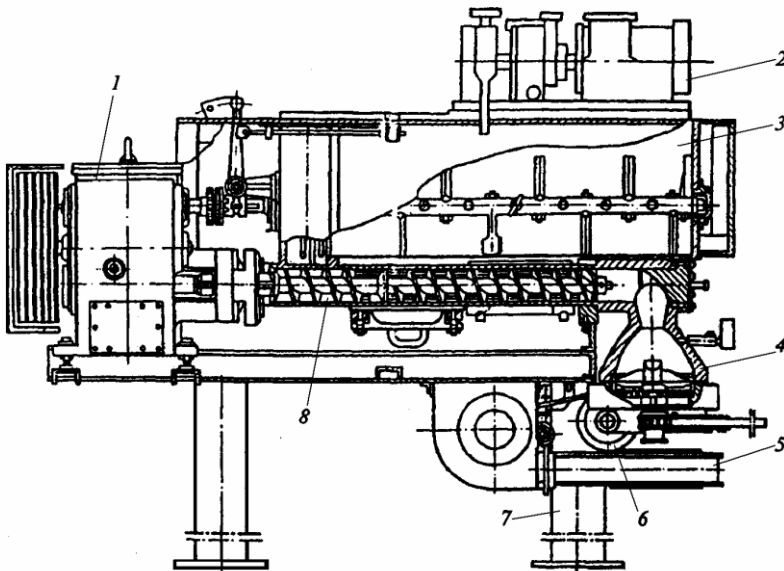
Шнековий макаронний прес ЛПЛ-2М: 1 – привід; 2 – дозуючий пристрій; 3 – тістозмішувач; 4 – пресуюча головка; 5 – обдувальний пристрій; 6 – механізм різання; 7 – станина; 8 – пресуючий корпус
